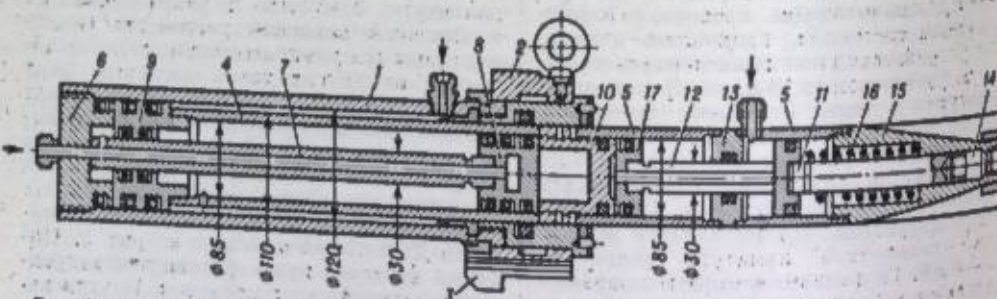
Гидродомкрат двойного действия ДГП-63-315: 1 — цилиндр тянущий; 2 — обойма; 3 — клин; 4 — внутр. цилиндр; 5 — цилиндр запрессовки; 6, 10 — заглушки; 7, 11, 12 — штоки; 8, 9, 17 — поршни; 13 — стенка; 14 — конус с шариком; 15 — оголовок; 16 — пружина.
